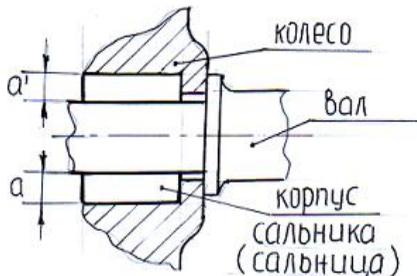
Схема проверки радиальной центровки ротора в корпусе насоса
